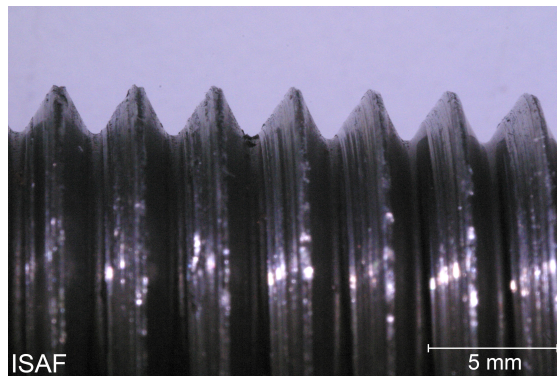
Gewindeprüfkörper axial belastet mit 160kN (Bolzen)
